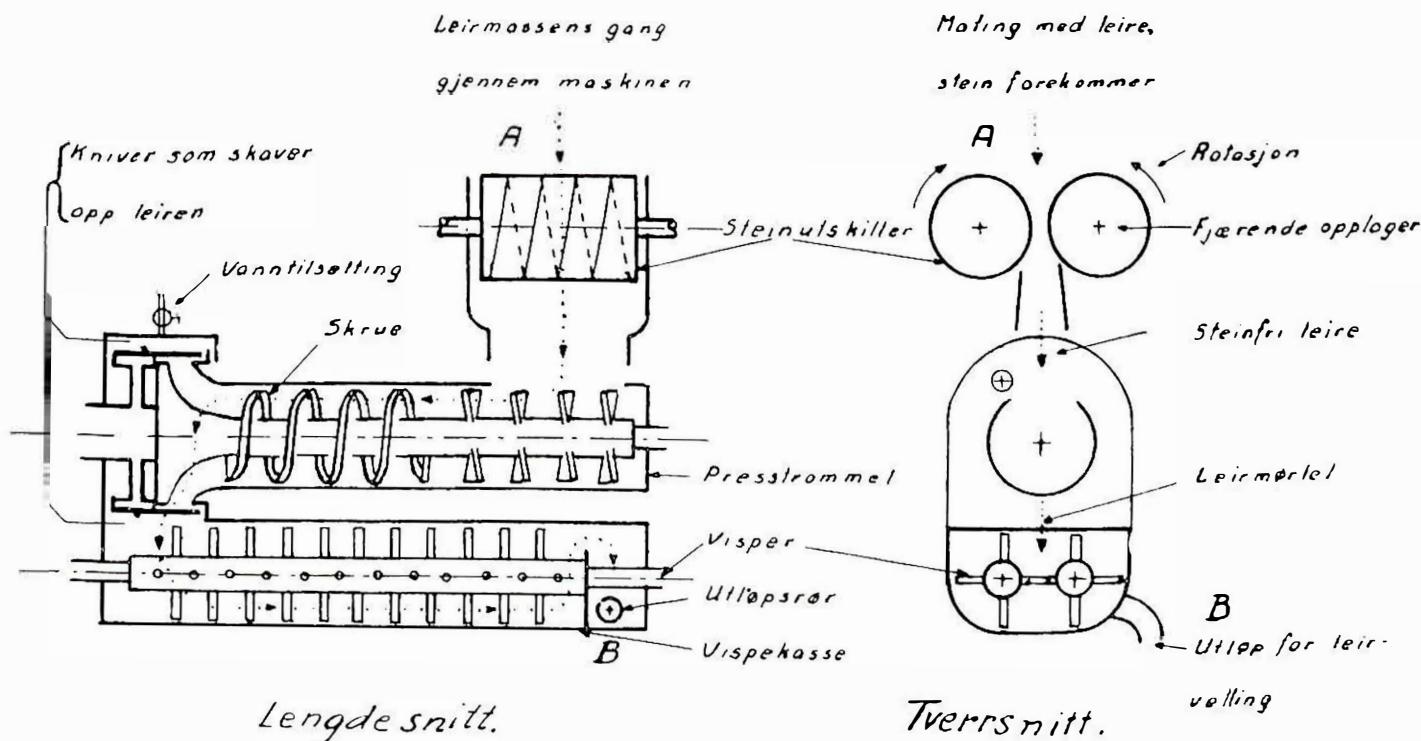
Prinsippskisse av leirmørtelmaskin. Maskinen drives av en motor som sittes på knivakselen og ved hjelp av tannhjul overføres kraften videre til steinutskiller, skrue og visper som alle roterer med forskjellig hastighet.
